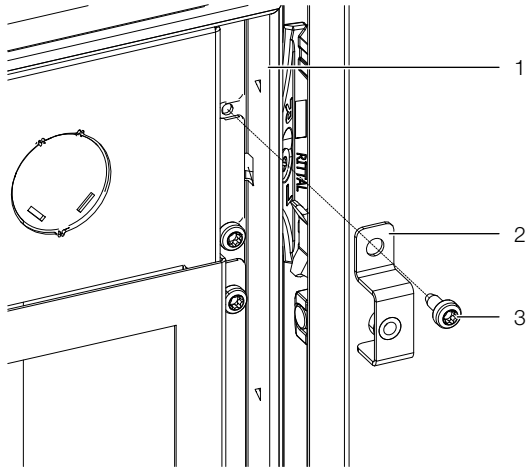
Montagewinkel zur Befestigung der Seitenwand
